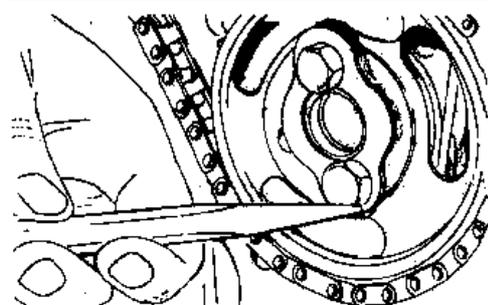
А.16. Отгибание лепестков стопорной пластины звездочки распределительного вала
